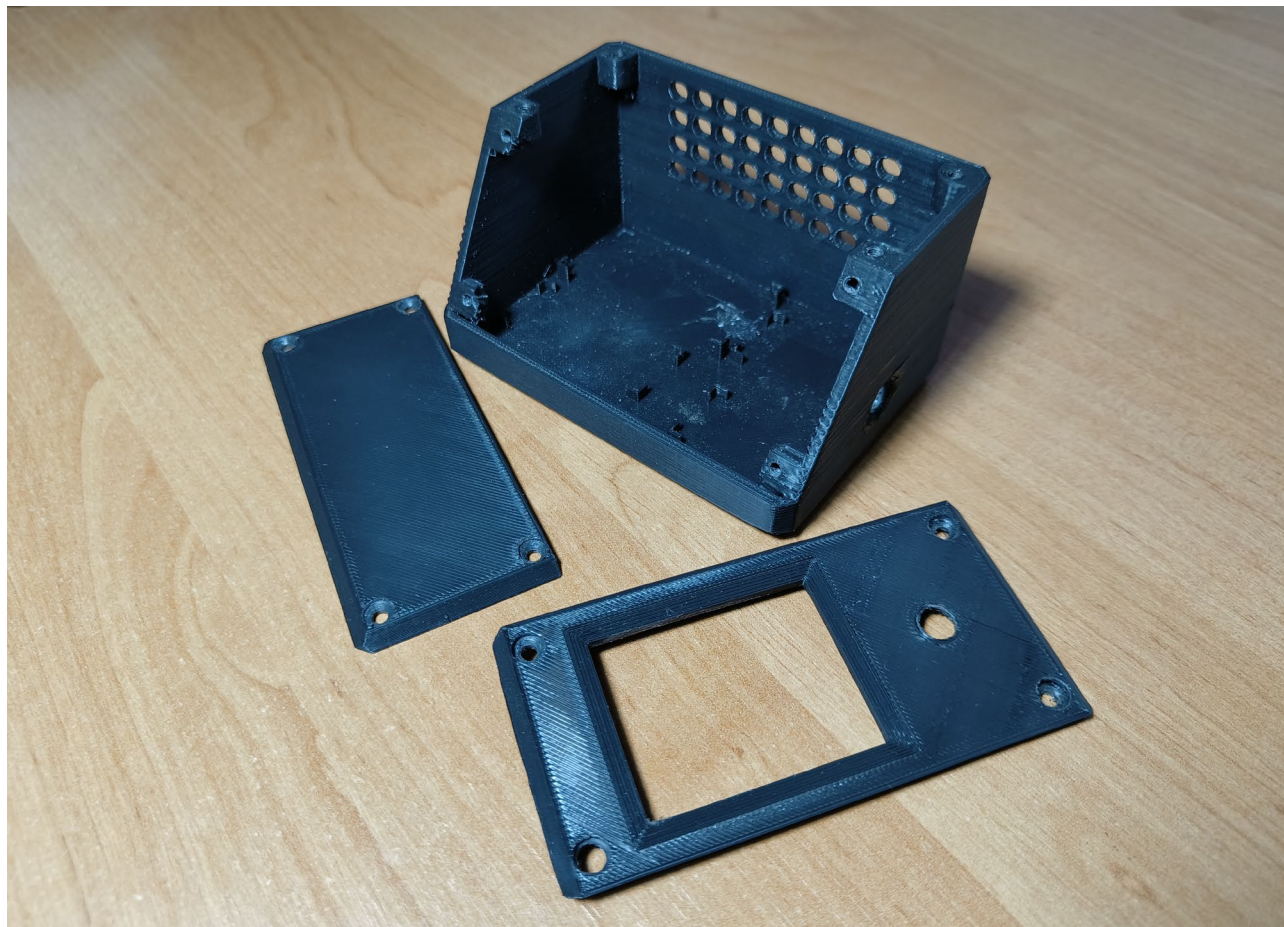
Роздруковані деталі корпусу перед монтажем
